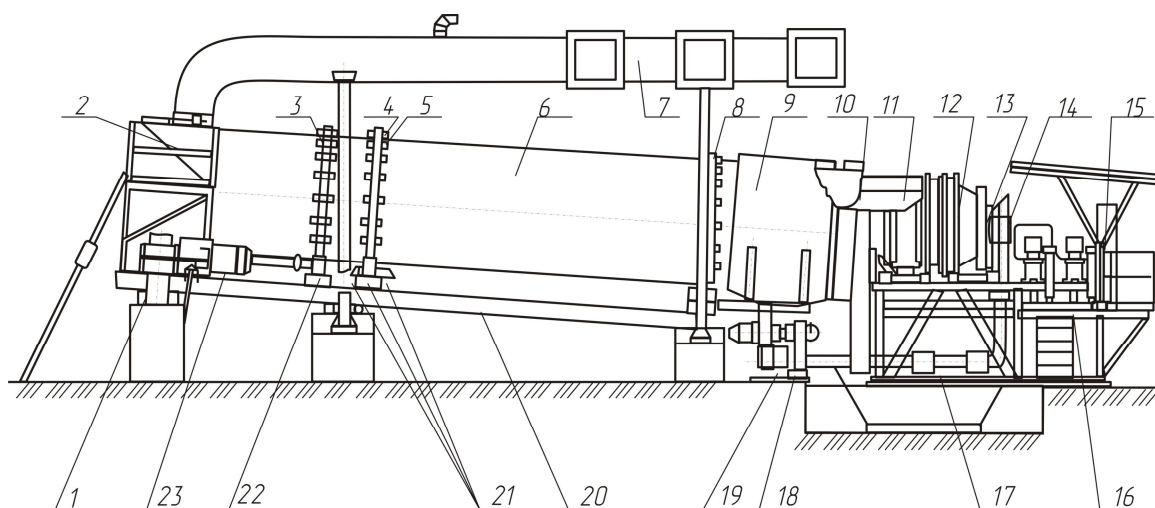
Сушильный барабан: 1 – редуктор; 2 – загрузочный короб с дымовой коробкой; 3 – зубчатый венец; 4, 8 – опорные бандажы; 5 – температурные компенсаторы; 6 – сушильный барабан; 7 – газоотводящая система; 9 – камера горячего воздуха; 10 – разгрузочный короб; 11 – топка; 12 – зажигательный конус; 13 – подогреватель; 14 – форсунка; 15 – пульт управления; 16 – площадка для персонала; 17 – воздуховод; 18 – вентилятор; 19 – электродвигатель вентилятора; 20 – рама; 21 – упорно-опорные ролики; 22 – ведущая шестерня; 23 – электродвигатель барабана
